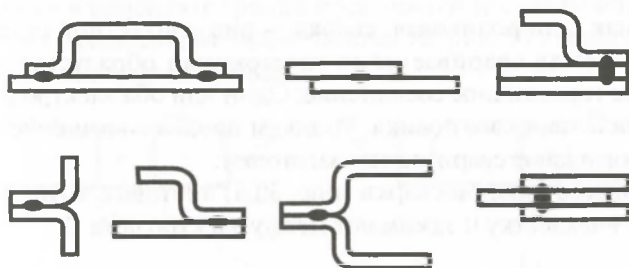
Примеры сварных соединений для точечной сварки
